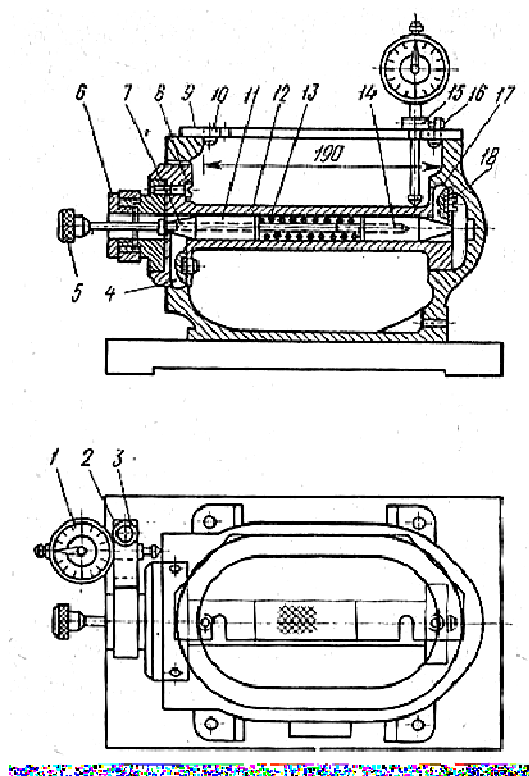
Приспособление для проверки параллельности оси вала и плоскости под блок цилиндров:
